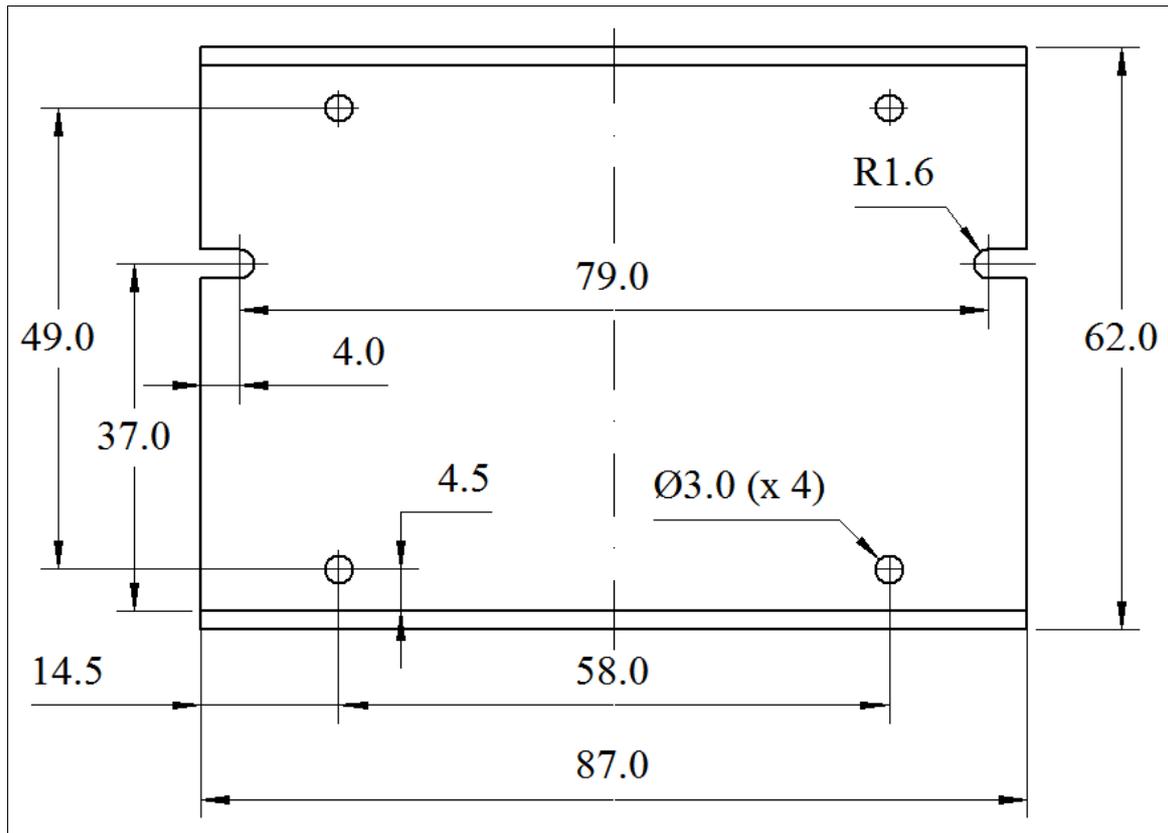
Maßbild Montageblech, Höhe = 30mm, Blechdicke = 2mm
